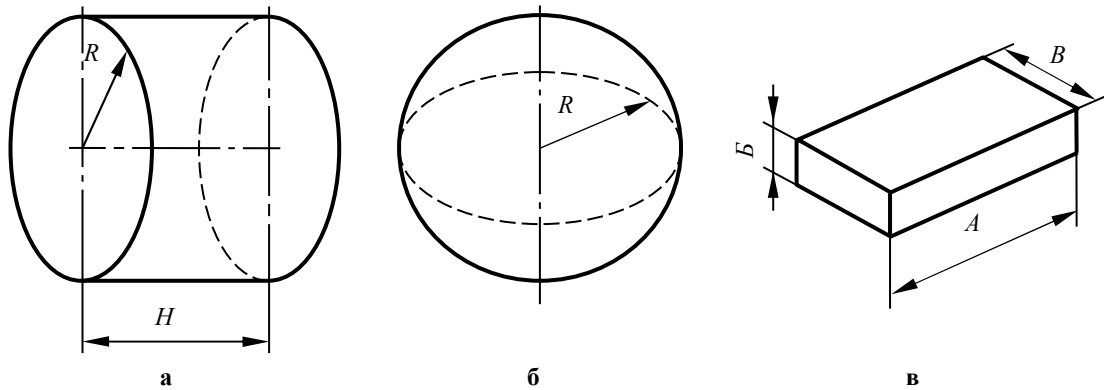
Эскизы элементов деталей: а – цилиндр; б – сфера; в – брус
